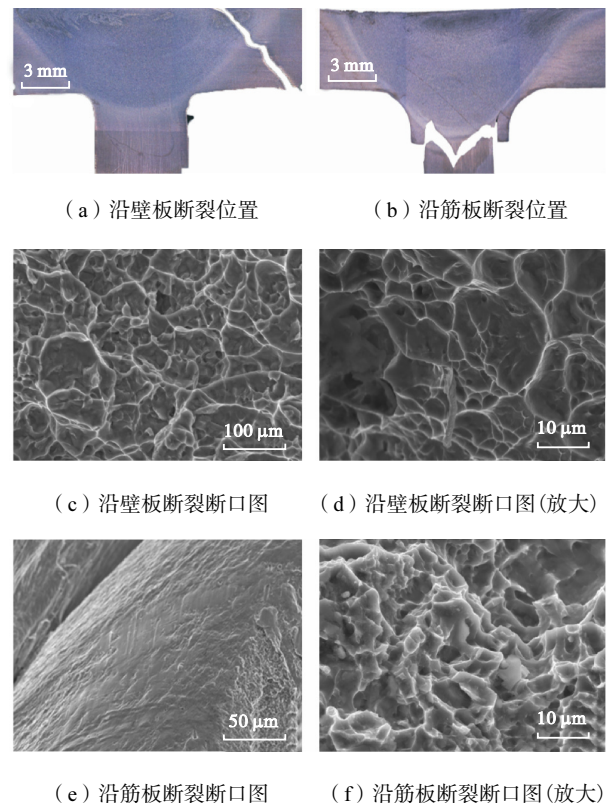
钛合金 T 形接头的拉伸断裂位置和断口形貌
